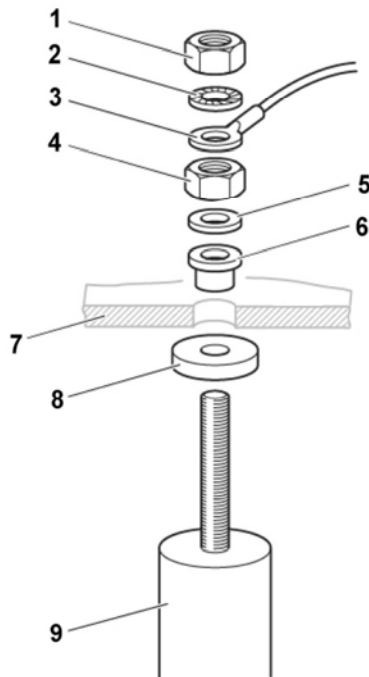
Aufbau der Befestigung einer Magnesium-Schutzanode
